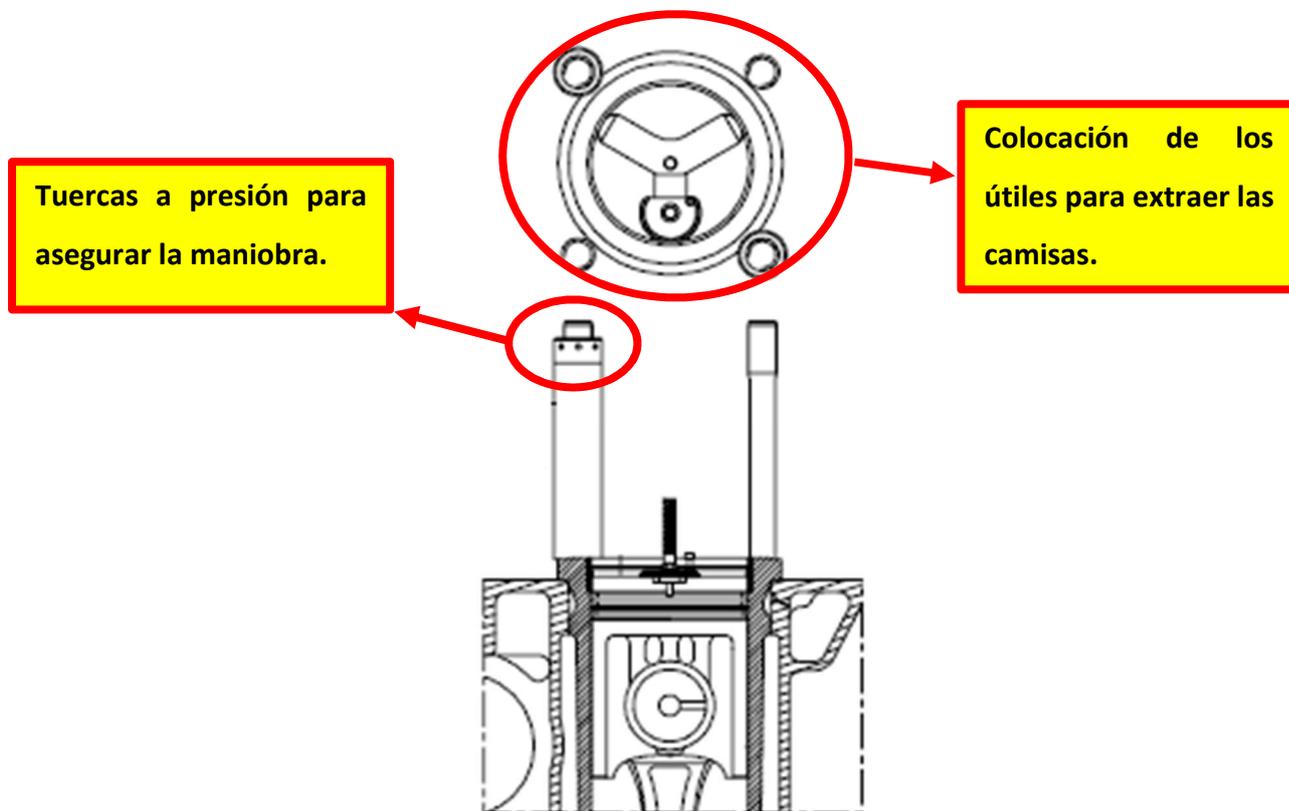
Detalle útil extracción de camisas. Fuente: Trabajo de campo.
